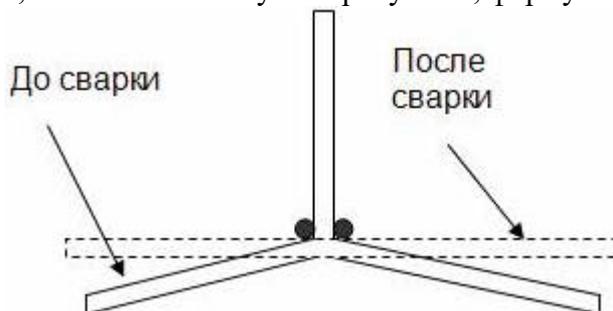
Обратный изгиб деталей перед сваркой
